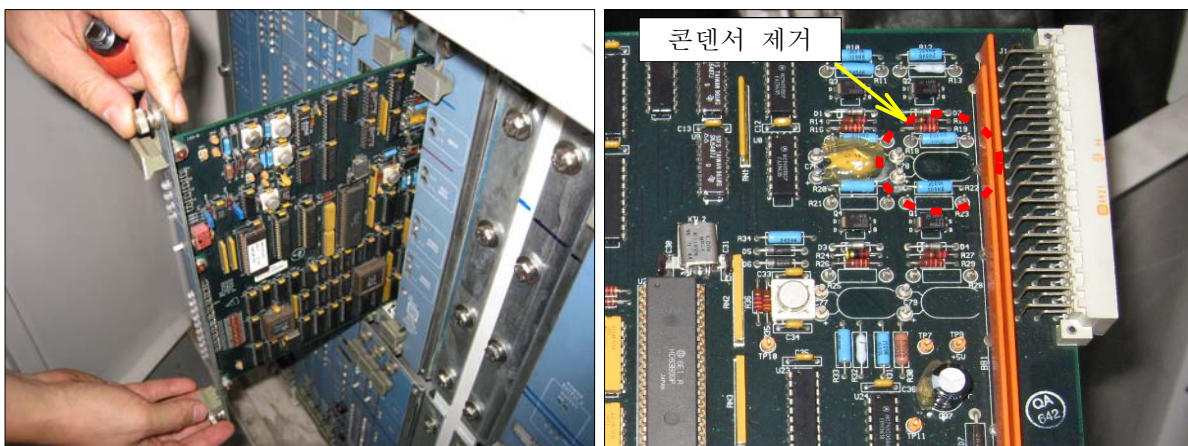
콘덴서가 제거된 디코더 PCB(FL)
